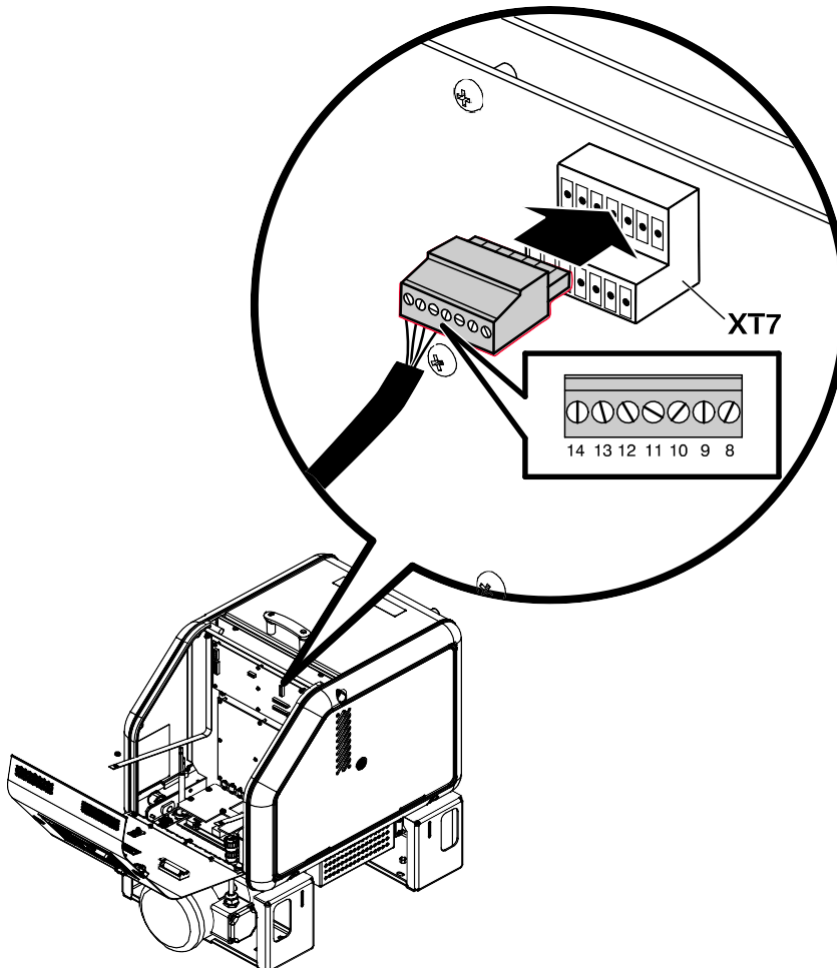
Entradas de fiação (A10/A16 apenas)
